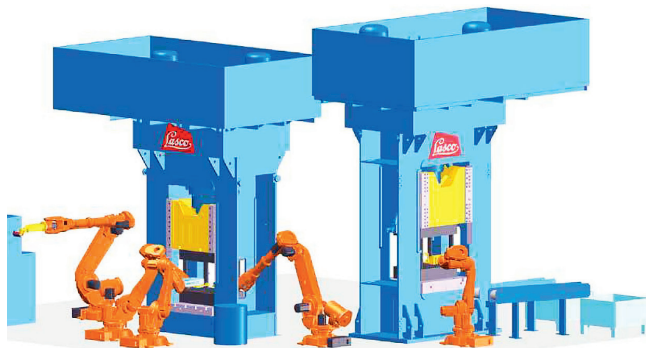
Общий вид в 3D роботизированной линии штамповки [7]
